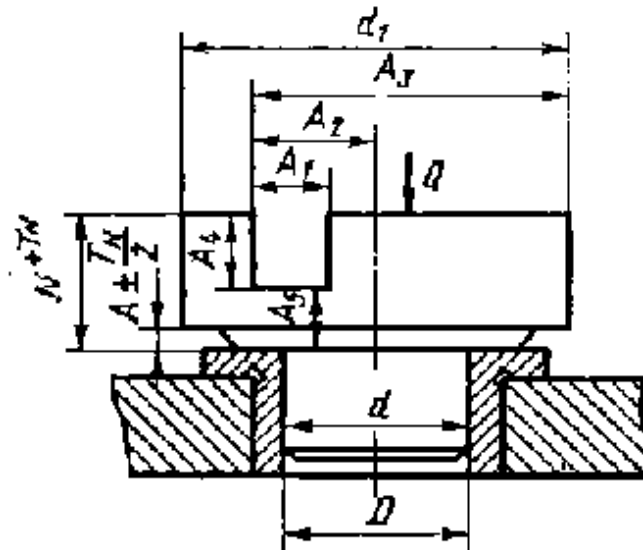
Схема установки заготовки при фрезеровании паза
